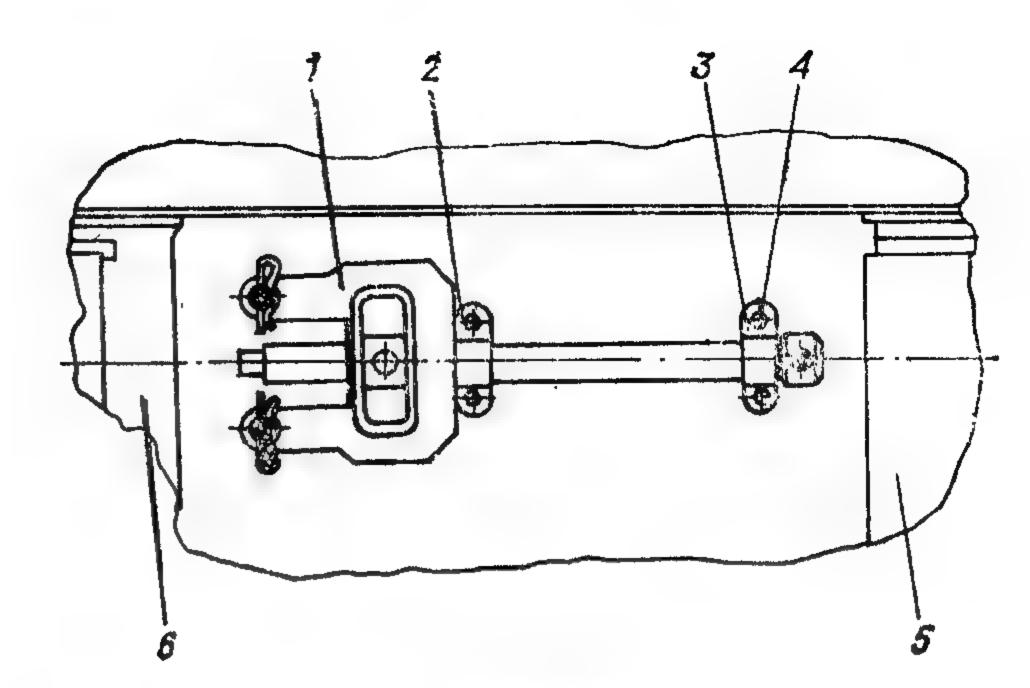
Установка приспособления для выпрессовки пальцев гусениц:
